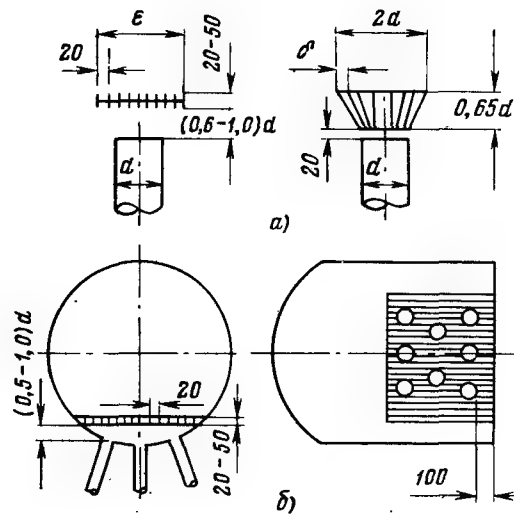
Схема установки жалюзийных решеток над опускными трубами:
